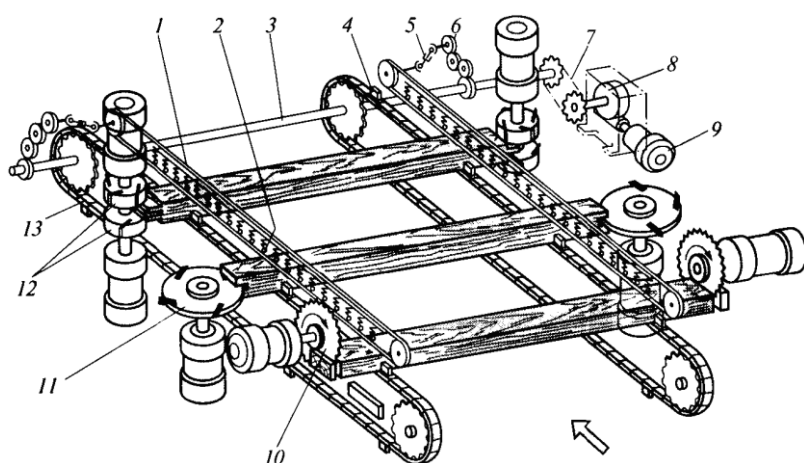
Двосторонній рамний шипорізний верстат: 1 – клиновий ремінь; 2 – ролик; 3 – вал; 4 – упор; 5 – карданна передача; 6 – зубчаста передача; 7 – ланцюгова передача; 8 – черв'ячний редуктор; 9 – електродвигун; 10 – пила; 11 – дискова фреза; 12 – шипорізні фрези; 13 – ланцюг
